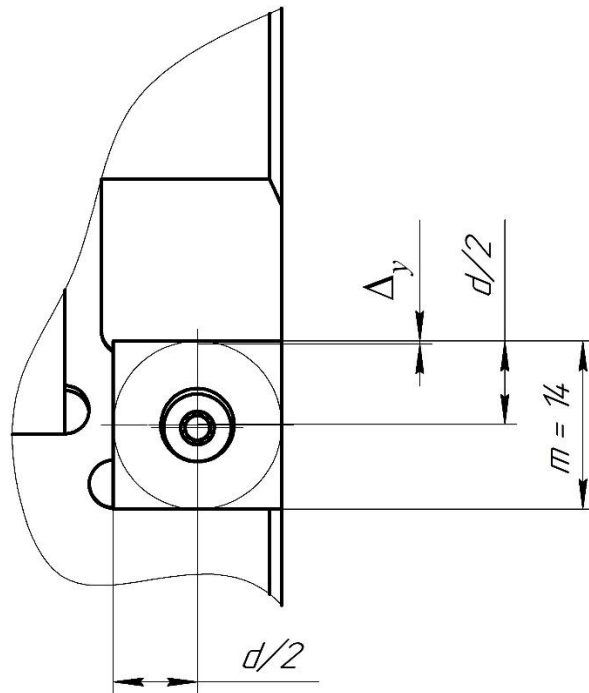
Схема розрахунку похибки базування пластини в кутовий паз.
